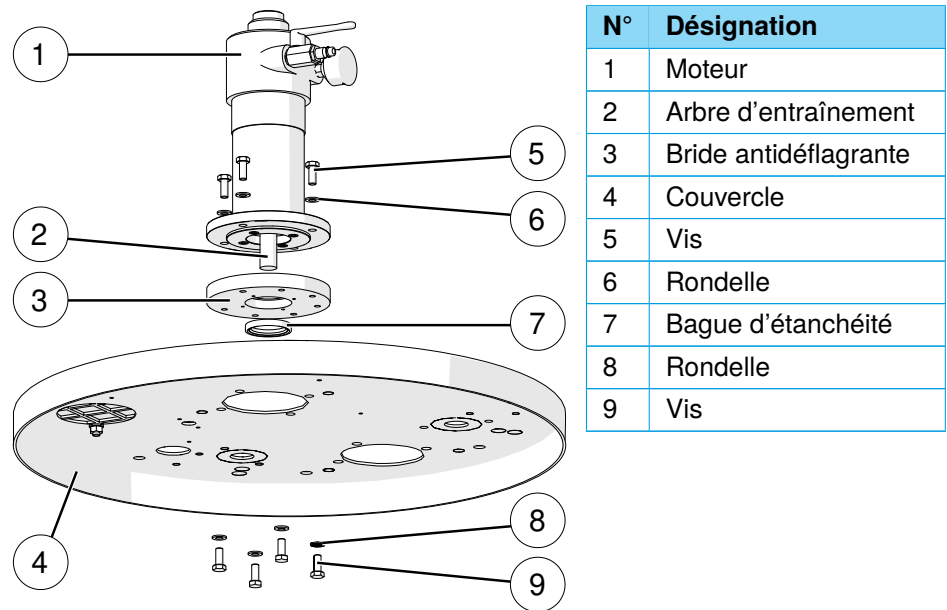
Montage du moteur à air comprimé sur couvercle
